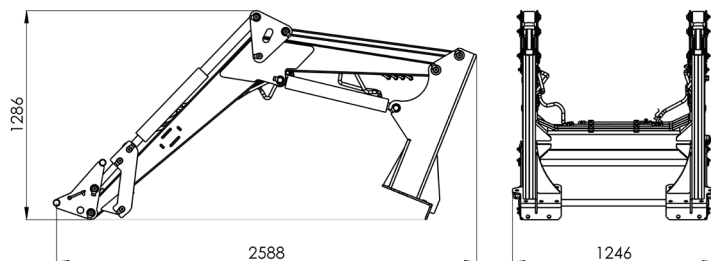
Размеры погрузчика, подготовленного для транспортировки как груз.
